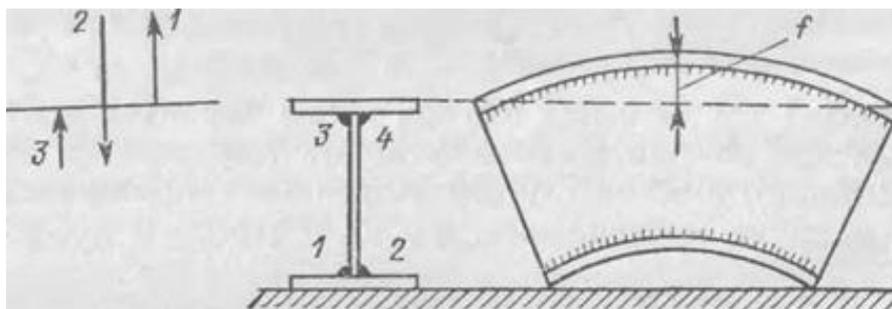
Деформация сварной двутавровой балки
